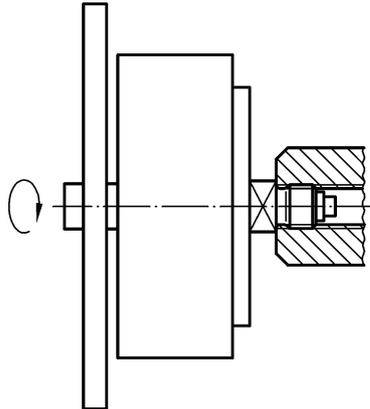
Torsionsprüfung — Manometer mit Anschluss rückseitig
